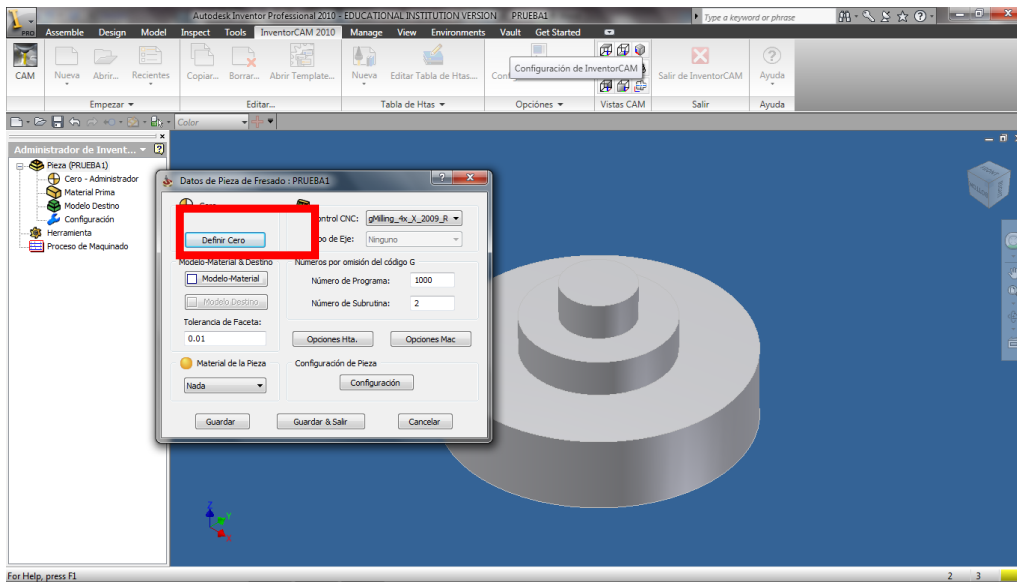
Maquinado Fresadora CNC – Definir Cero
